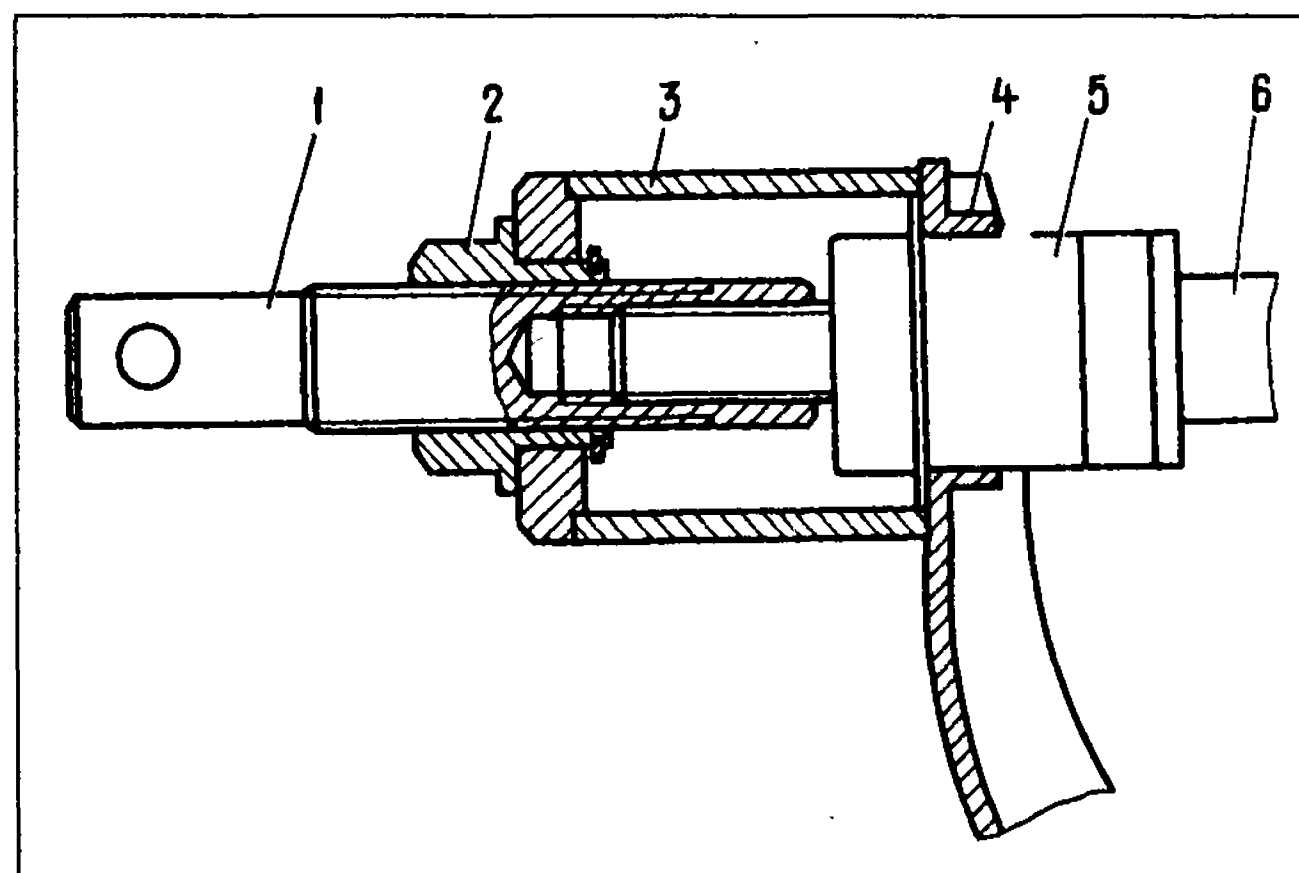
Схема выпрессовки шарнира нижнего рычага с помощью приспособления 02.7823.9500: 1-винт; 2-гайка; 3-стакан; 4-нижний рычаг; 5-шарнир; 6-ось нижнего рычага
